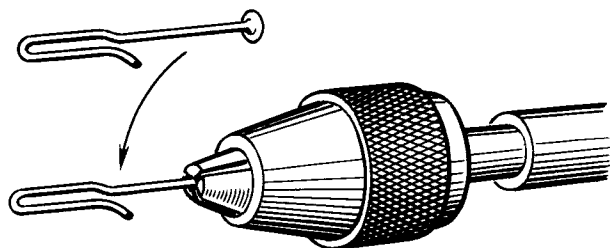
Приспособление для закручивания резиномотора с помощью ручной дрели
